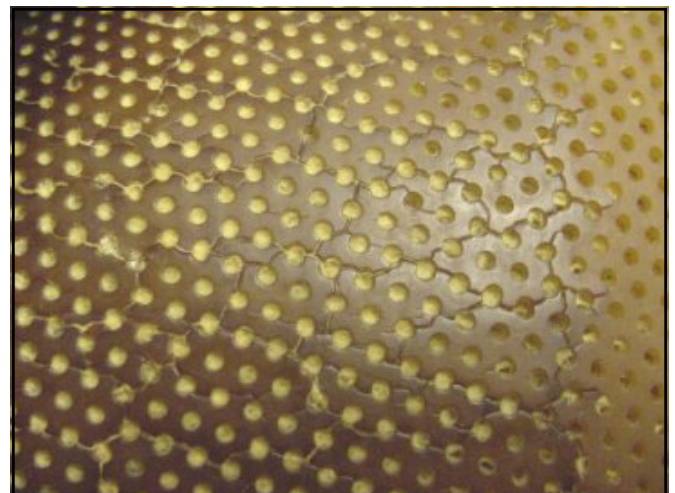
La severidad de las grietas en el lado de la manta puede ser reducida con la indexación de la manta.
